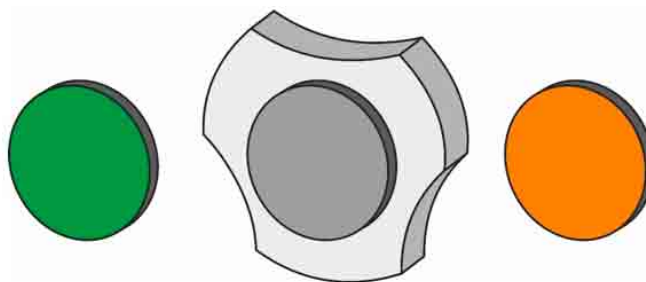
Второй вариант конструкции – цельная форма со сменными вкладышами
